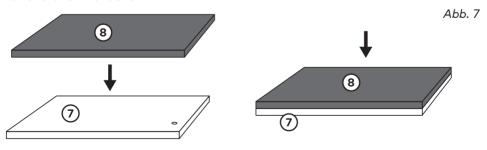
Folie vom *Dachbelag* (8) entfernen und passgenau auf die *Dachplatte* (7) aufkleben. Mit einem dicken Buch o. ä. beschweren, sodass der Belag gut angepresst wird.
